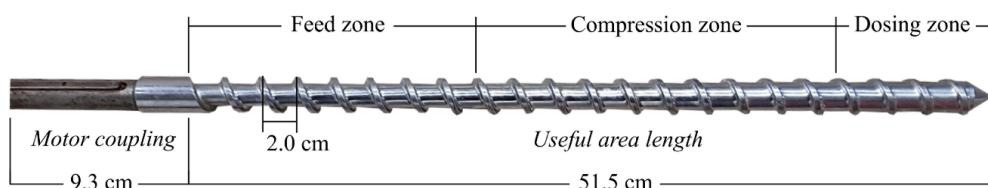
Tornillo extrusor Brabender® de una pieza, relación de compresión 3:1
